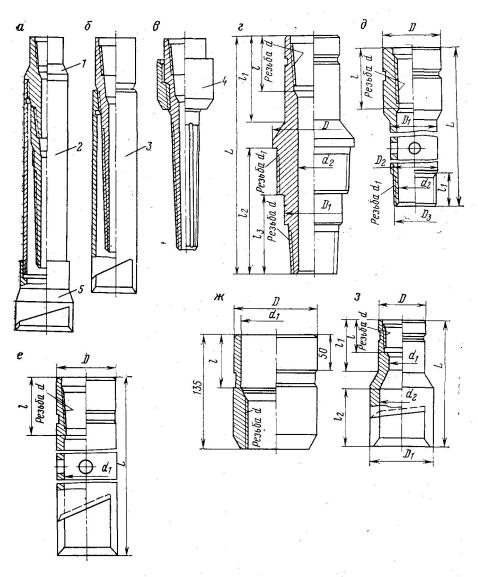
Центрирующие приспособления к ловильному инструменту:
